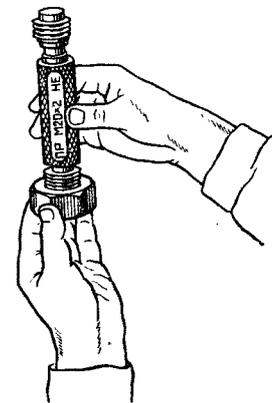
Прием проверки внутренней резьбы резьбовым калибром-пробкой
